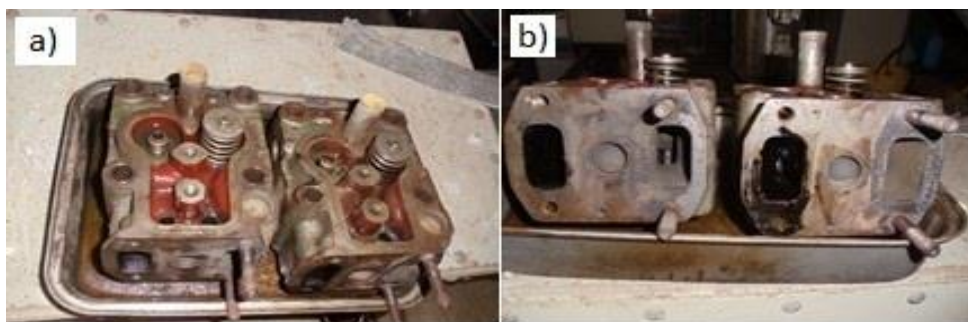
a) Vista de topo do Cabeçote de um motor MWM, contaminado pelo alcatrão. b) Vista Lateral do cabeçote de um Motor MWM, contaminado pelo alcatrão.
